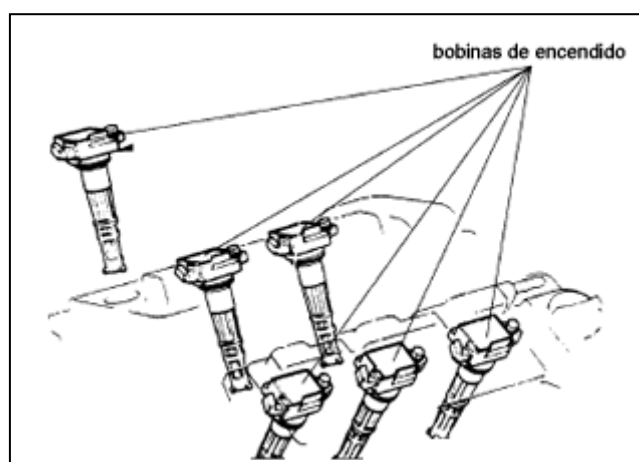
Sistema DIS implantado en un motor en "V" de 6 cilindros.
